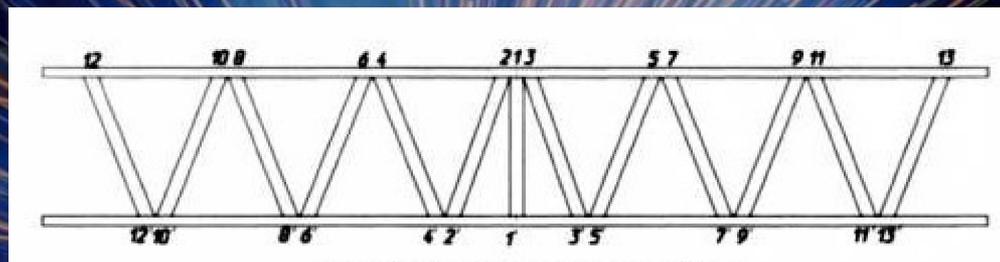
Порядок выполнения сварки фермы несущей
